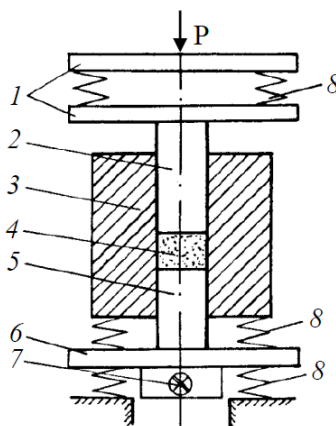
Схема вибрационного прессования: 1- плиты; 2 – верхний пуансон; 3 – матрица; 4 – прессовка; 5 – нижний пуансон; 6 – опорная плита; 7 – вибратор; 8 – пружины
